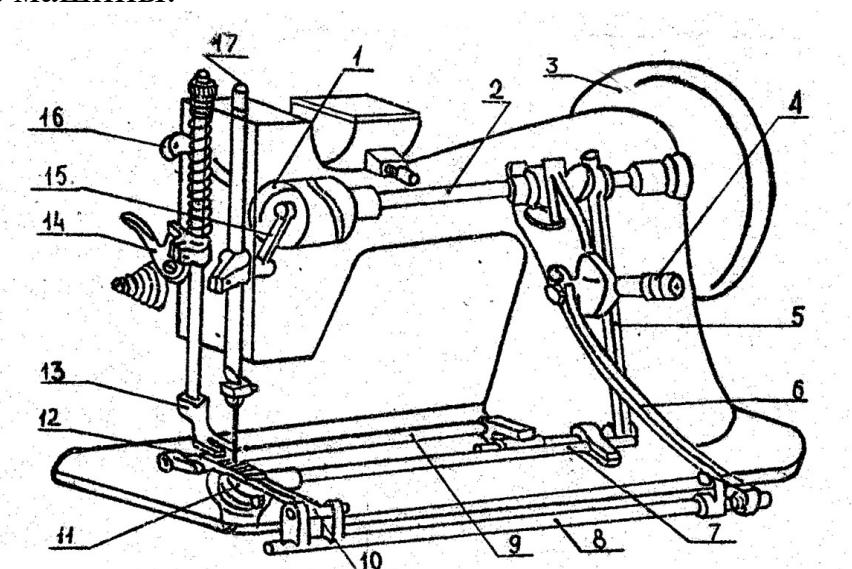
Конструктивная схема головки походной машинки 323 класса:
